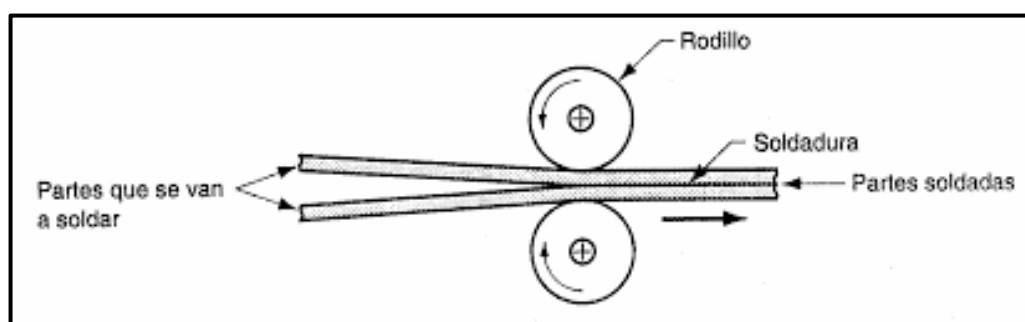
Proceso de soldadura por rodillos. Fuente: Universidad del Bio-Bio de Chile
